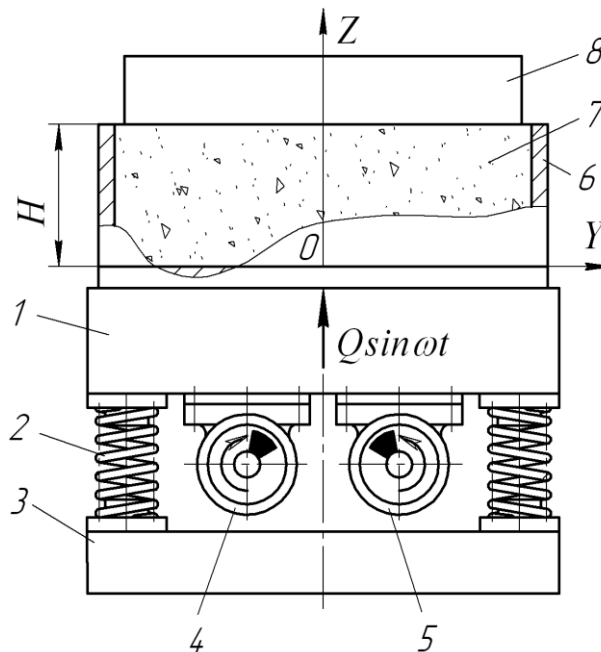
Расчетная схема динамической системы "виброплощадка - цементобетонная среда - пригруз" при вертикально направленных колебаниях: 1 – форма; 1 – подвижная рама; 2 – упругие опоры; 3 – опорная рама; 4, 5 – вибровозбудители колебаний; 6 – форма; 7 – бетонная смесь; 8 – пригруз.
